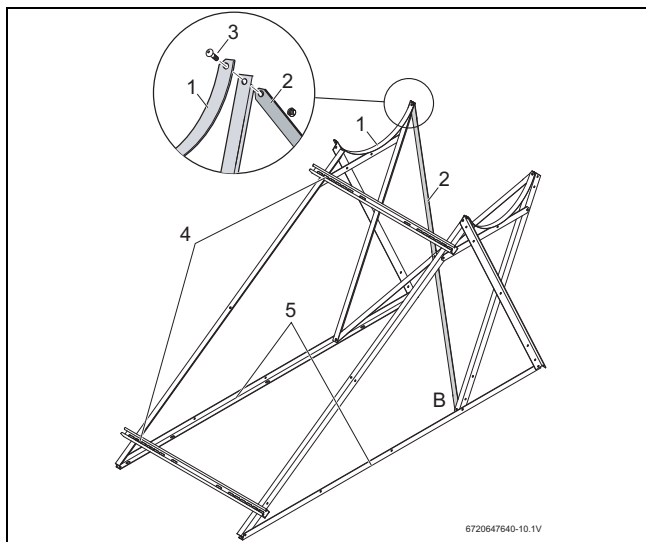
Atornillar los perfiles de cubierta plana/tejado inclinado
